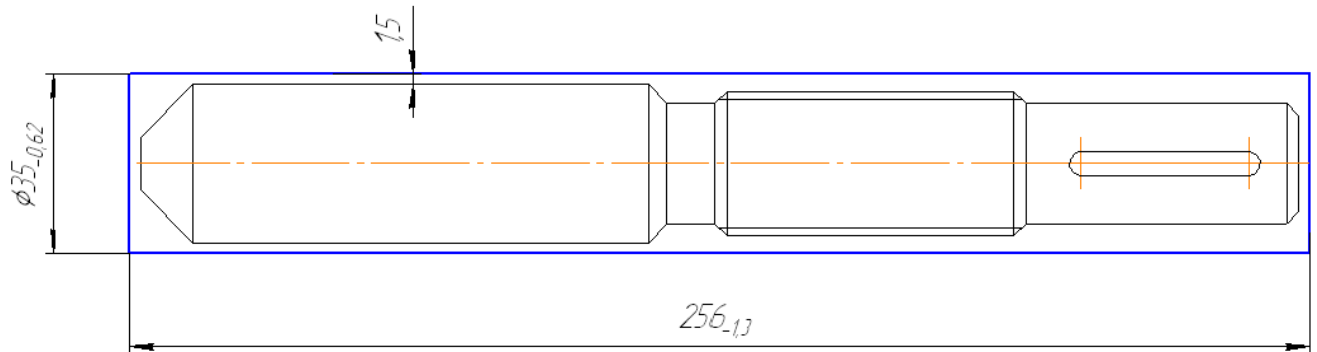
Ескіз заготовки з круглого прокату
